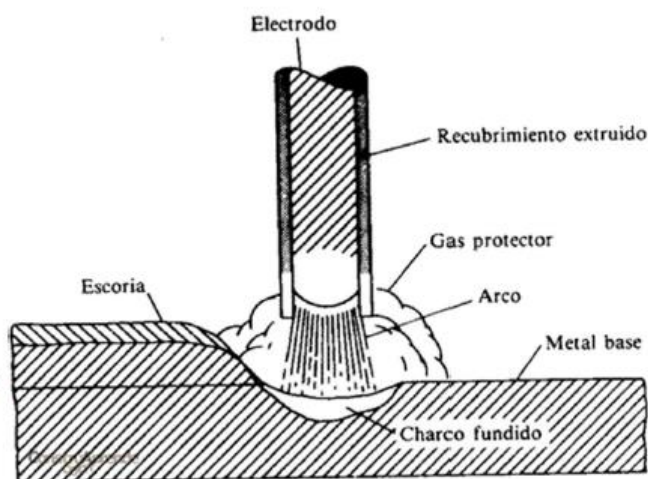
Soldadura por arco manual con electrodos revestidos.
